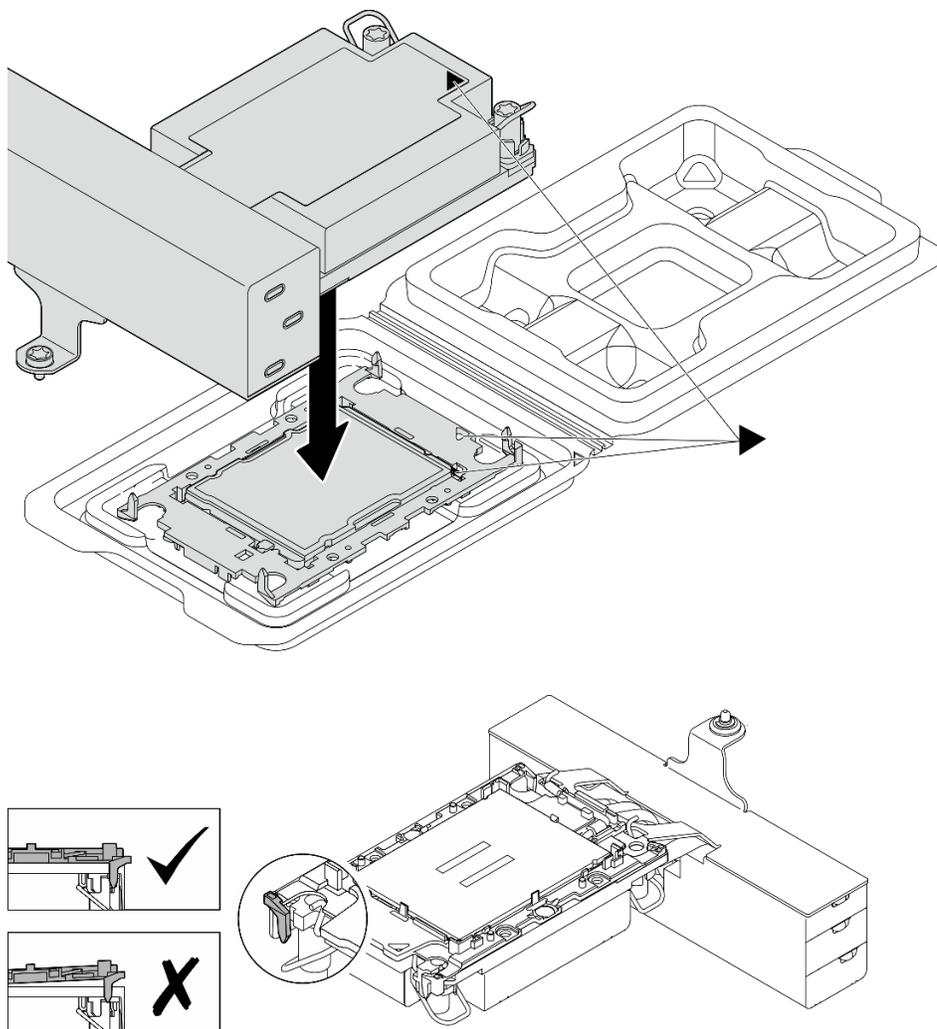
Assemblage du module de processeur-dissipateur thermique avec le processeur dans le support de transport
